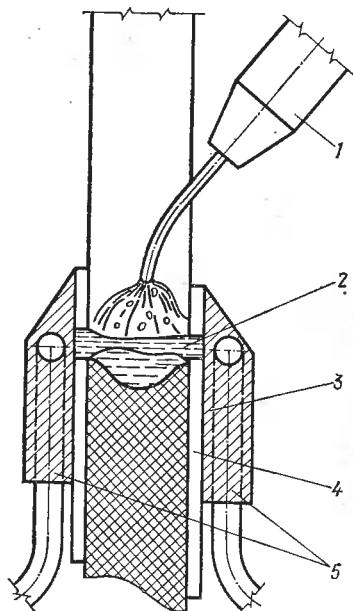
Схема формирования шва при сварке на вертикальной плоскости:
